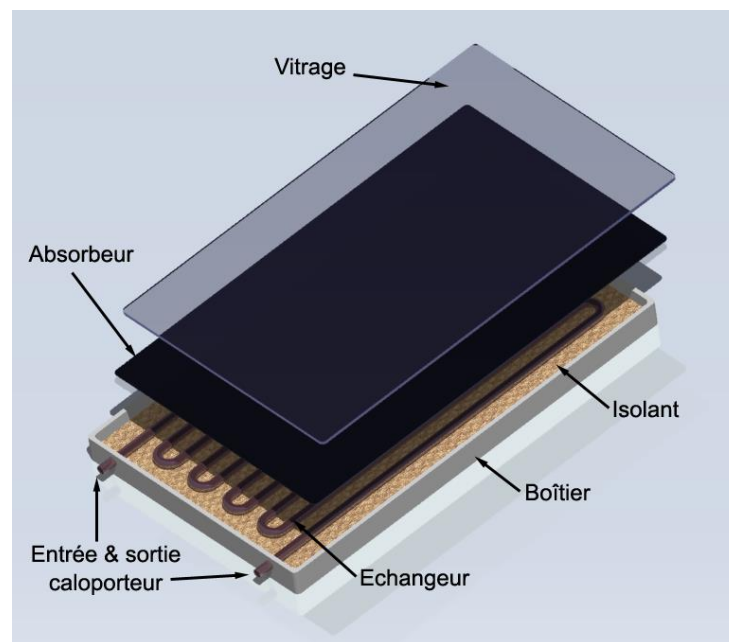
Constitution d'un capteur ou collecteur plan [23]
